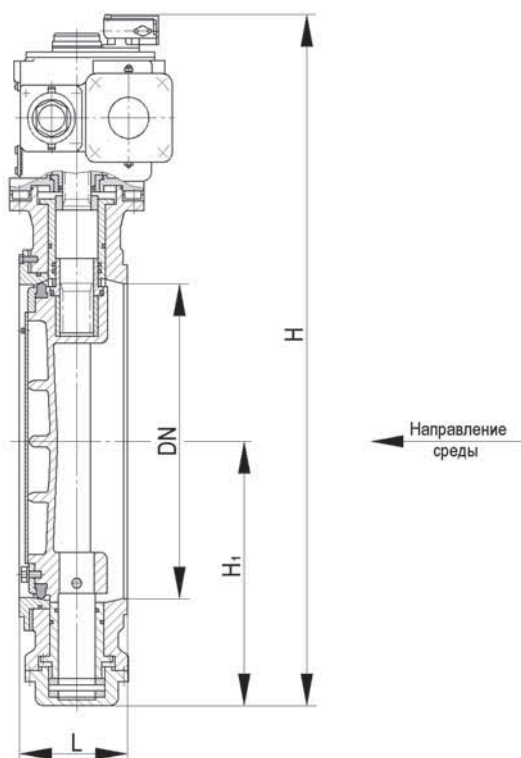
Затвор поворотный дисковый с пневмоприводом
